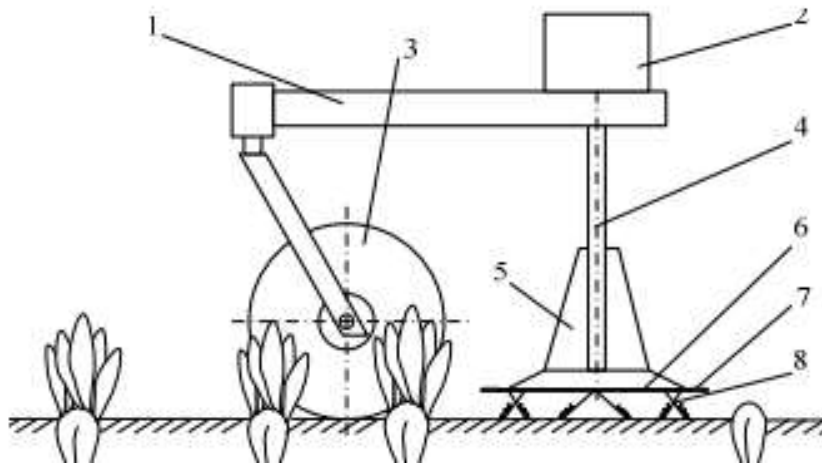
Апарат для зрізування гички та очищення головок коренеплодів: 1 — рама; 2 — редуктор; 3 — опорне колесо; 4 — вал; 5 — бітер; 6 — диск; 7 — ніж; 8 — очисний елемент.
